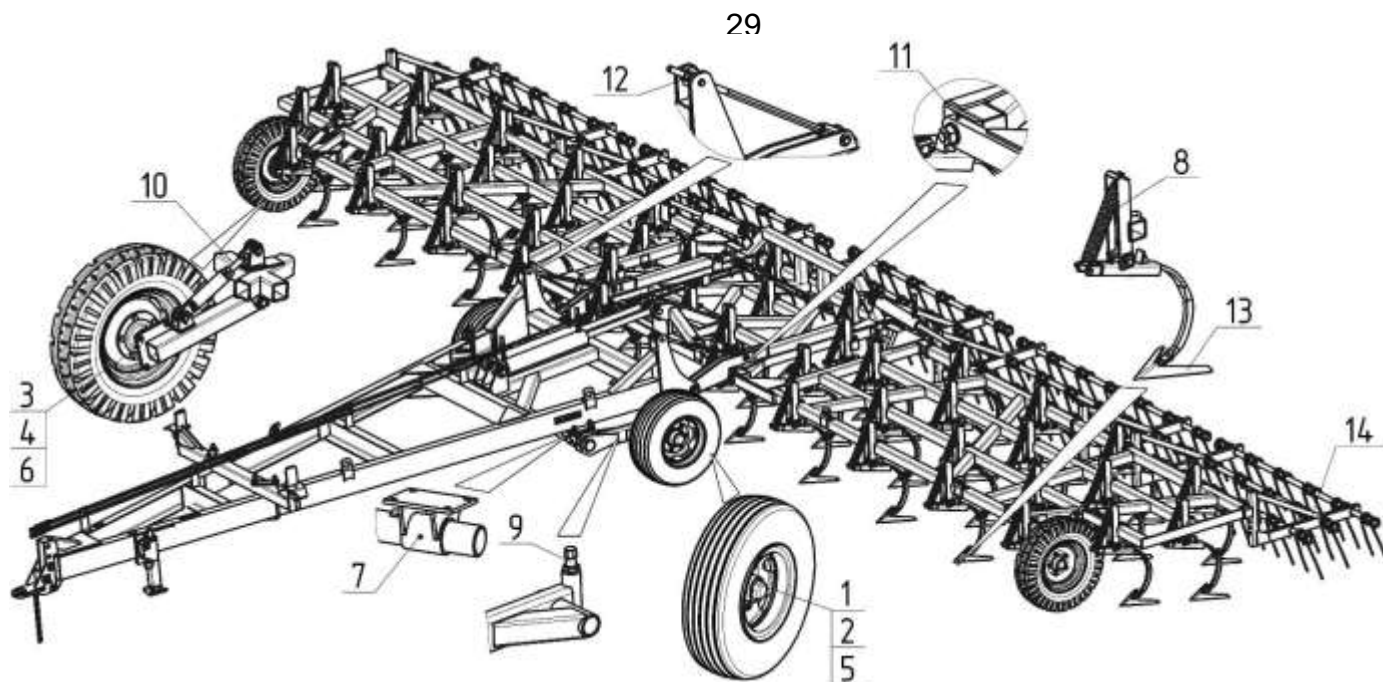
Места смазки. Схема расположения подшипников и манжет
